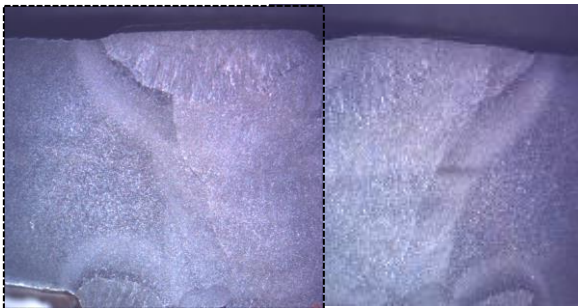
Macrografía aumento 10X, Cordón de soldadura con Cascarilla de acero.
